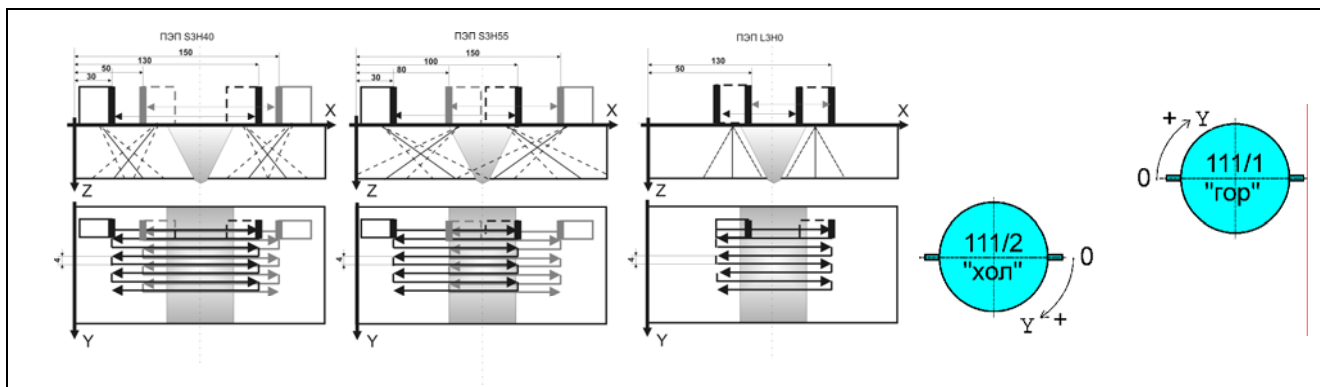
Схемы прозвучивания сварного соединения Ду1200: слева поперек СС, вдоль СС
